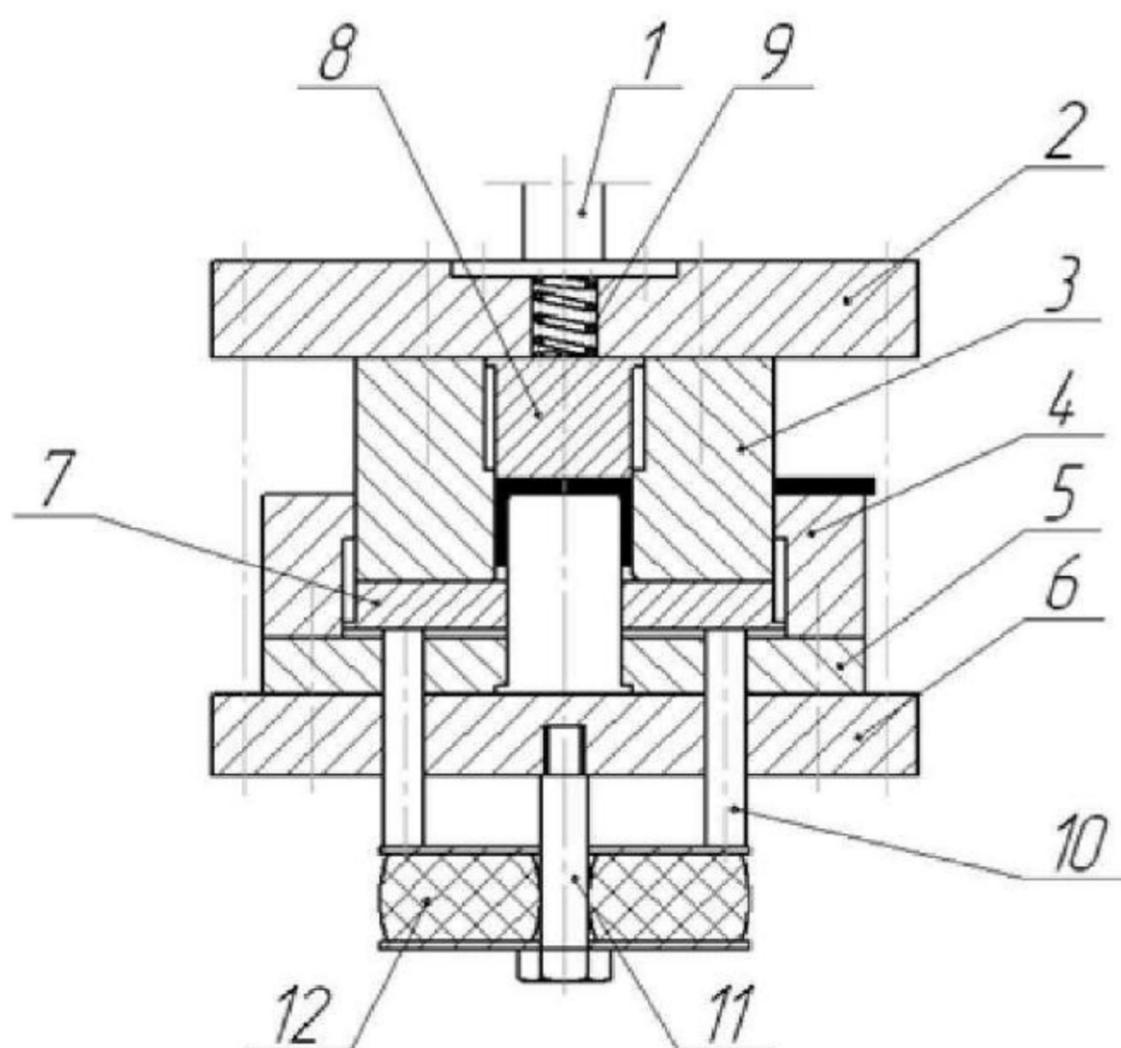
Схема штампа совмещённого действия для отрезки и гибки
